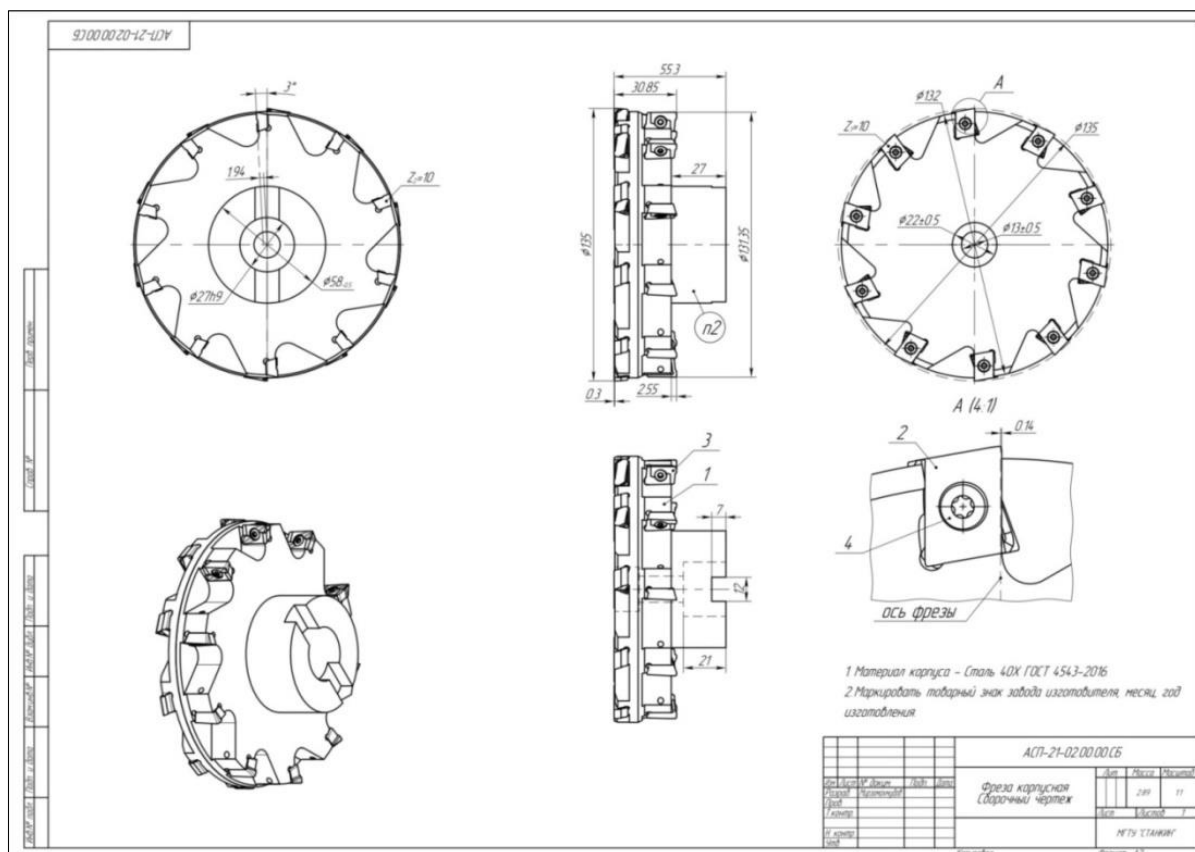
Сборочный чертеж дисковой фрезы с СМП
